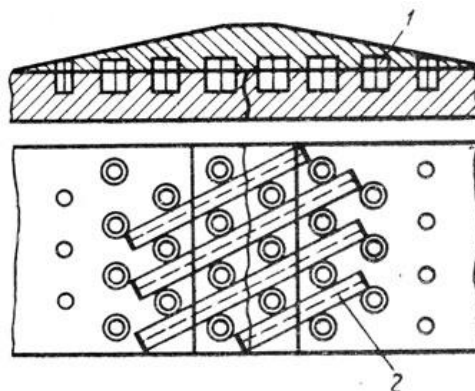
Схема расположения стальных связей в металле шва при холодной сварке чугуна: 1 - шпильки, 2 - стальные связи
